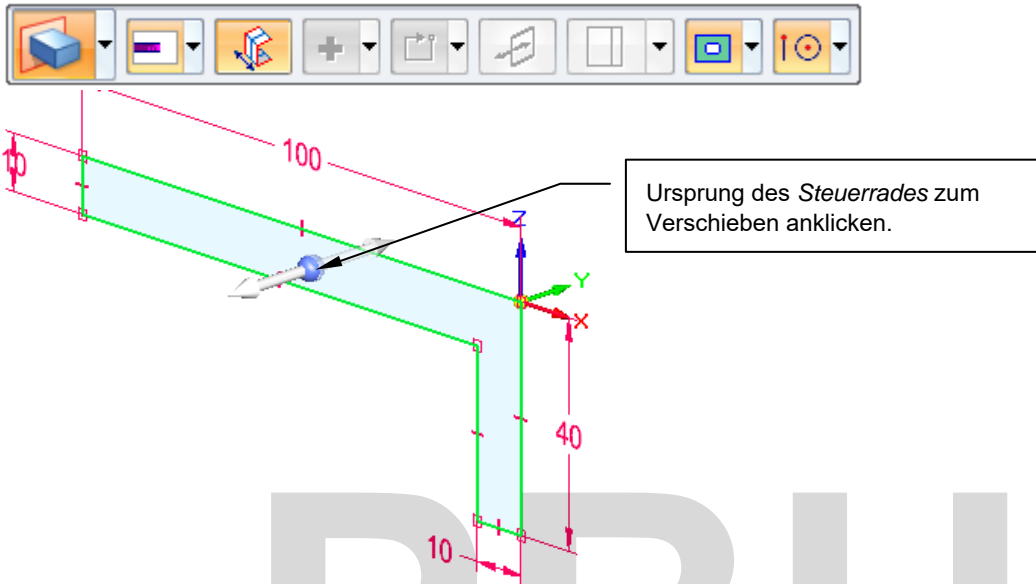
Der Bereich mit dem Extrusionswerkzeug
